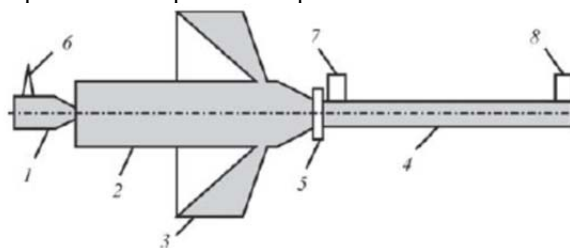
Схема багатоканального детонаційно-газового пристрою: 1 – форкамера для ініціювання процесу детонації; 2 – основна циліндрична камера; 3 – кільцева камера зі щільним виходом в циліндричну камеру; 4, 5 – вузол подачі порошку; 6 – запальник; 7 і 8 – п'єзоелектричні датчики тиску
